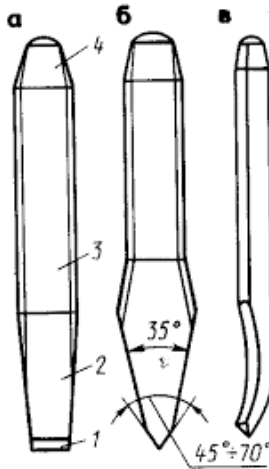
Інструменти для рубання: *а* – зубило;
